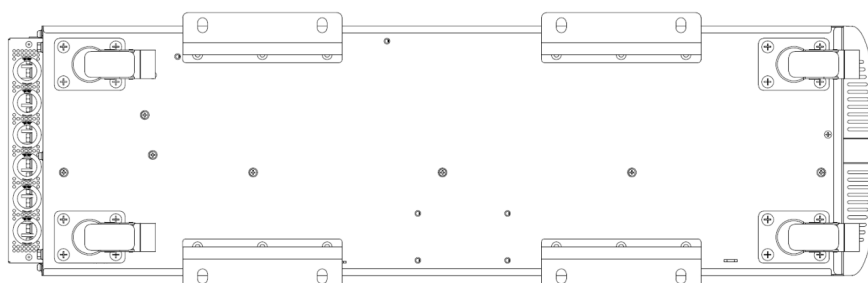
Widok przykładowego zasilacza po demontażu opakowania
